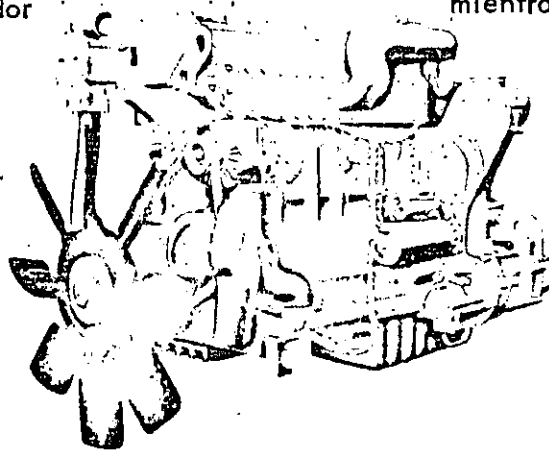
Motor Caterpillar de Diesel D343 (1988)
